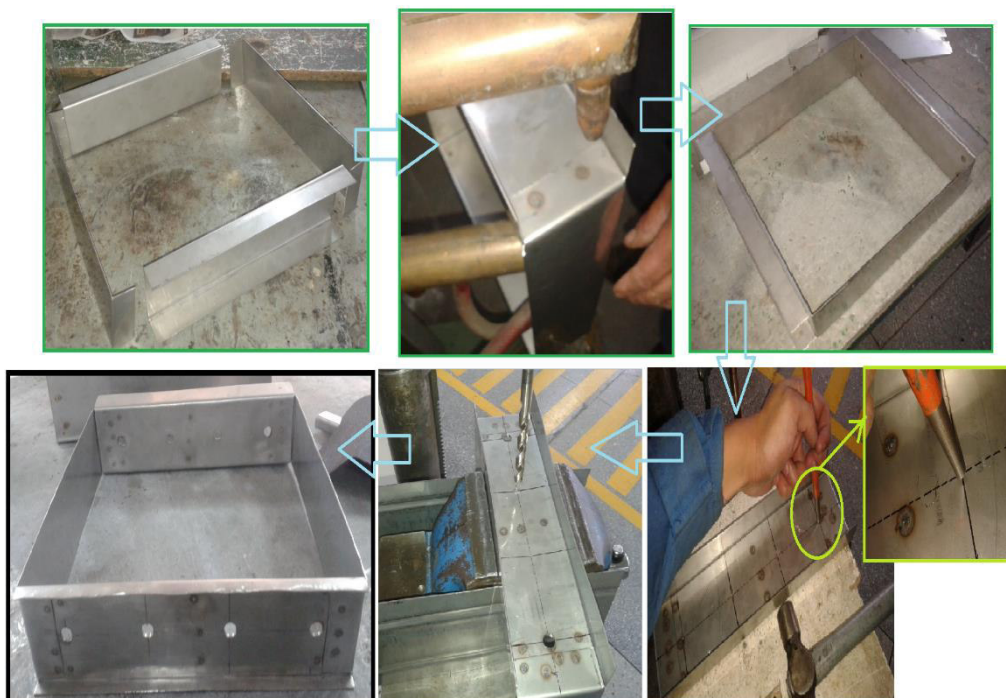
Proceso de elaboración para el cuadro soldado
